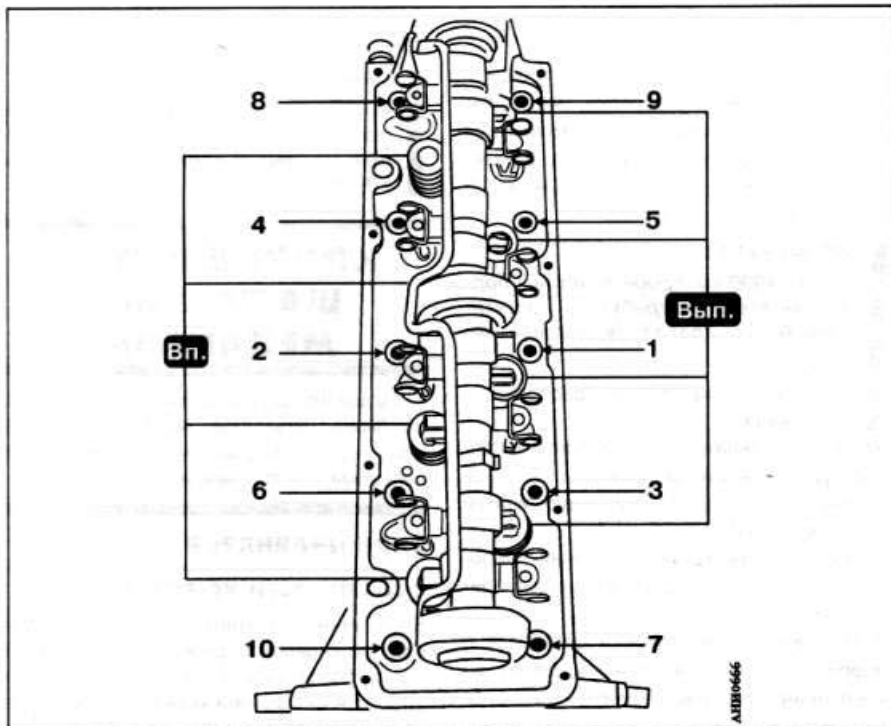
Порядок затяжки болтов крепления головки цилиндров и расположение клапанов
